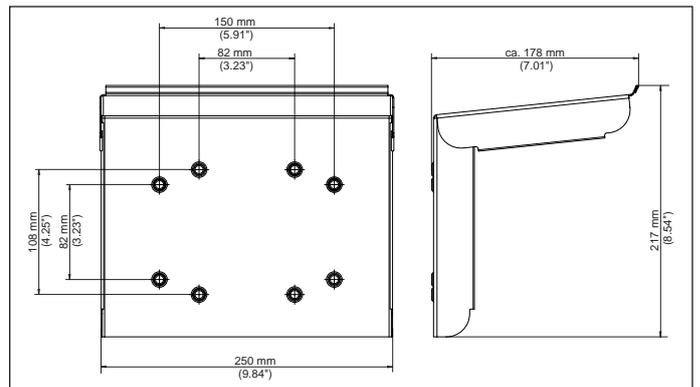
Dimensioni protezione dall'irradiazione solare VEGAMET 861, 862
